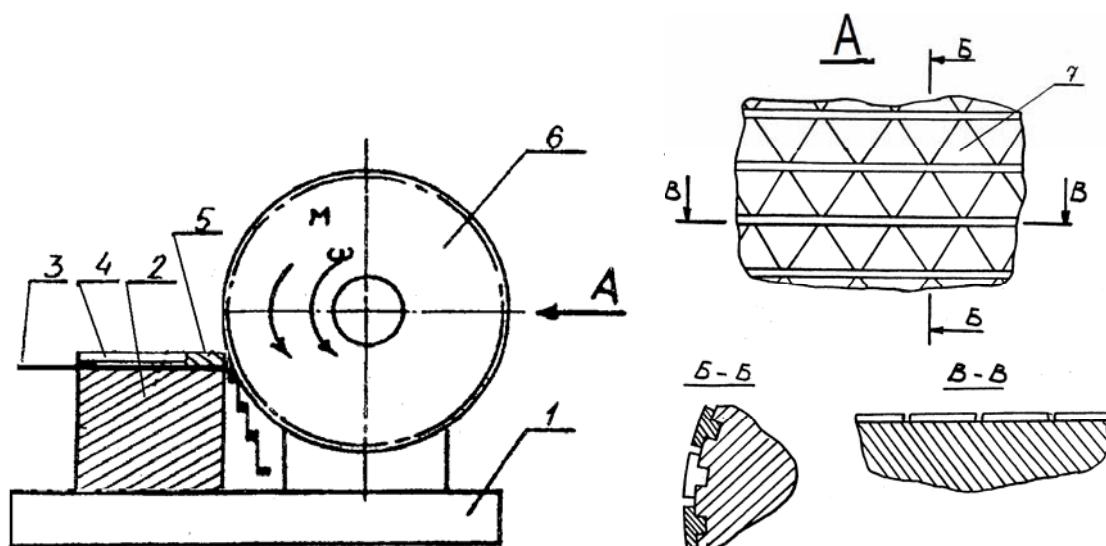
Схема установки для изготовления просечно-вытяжной сетки из листового материала.
